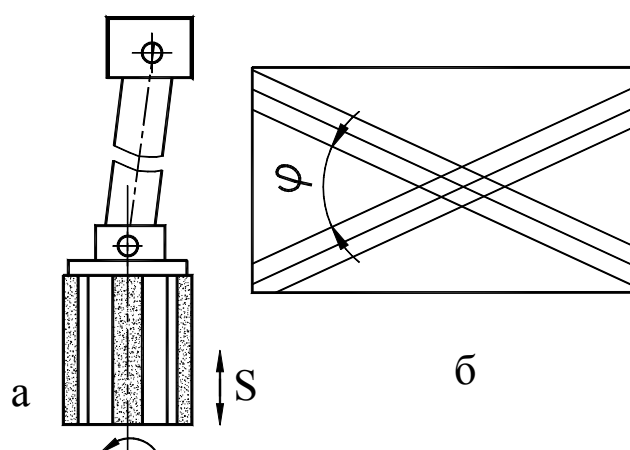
Хонингование: а – хонинговальная головка; б – траектория движения инструмента (развертка отверстия)
